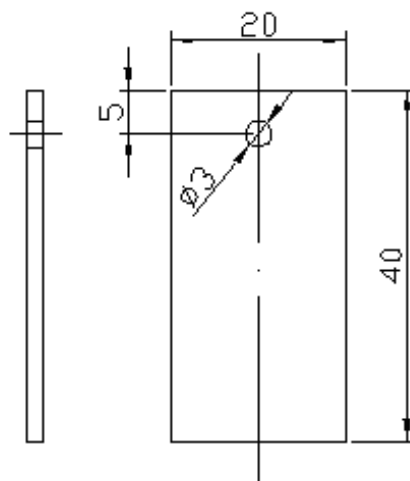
Форма и размеры конструкционного материала (пластинка)
